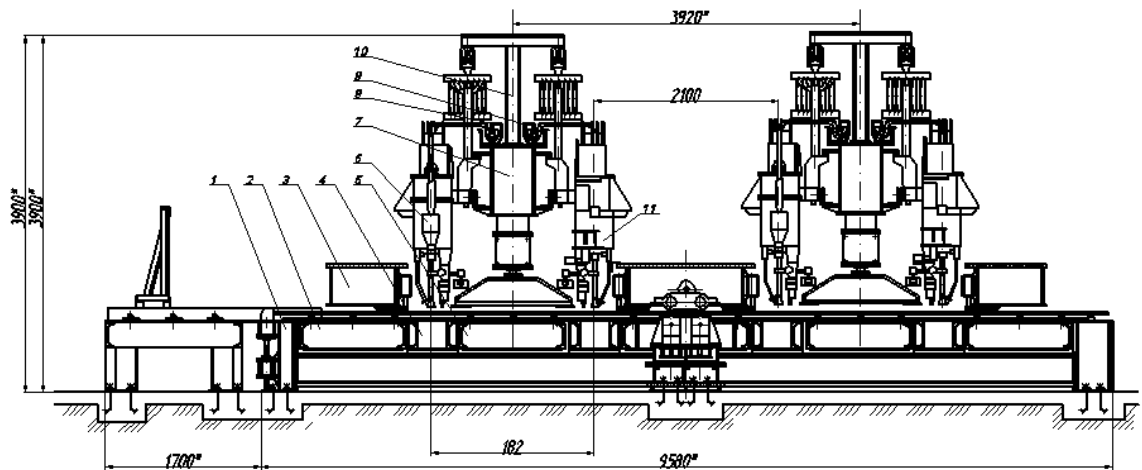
Установа для зварювання листових заготовок цистерни
